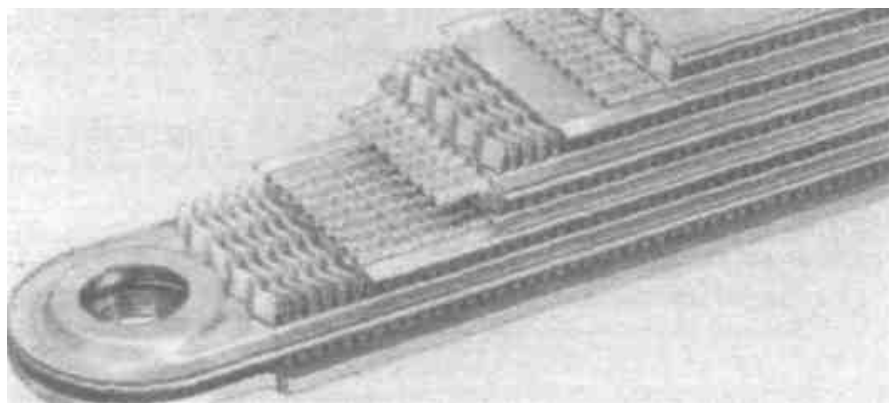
Схема ПРТ зі штампованими проставковими листами для формування вбудованого колектора
